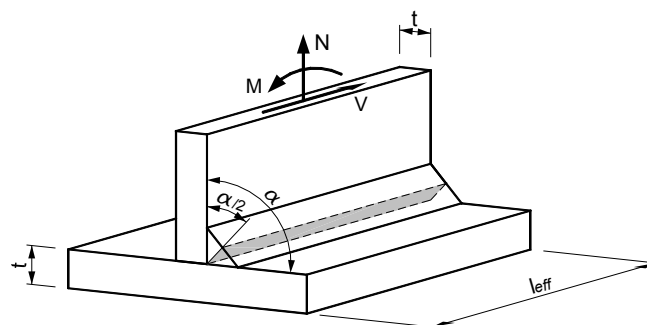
Definition der wirksamen Schweißnahtlänge  $l_{eff}$
